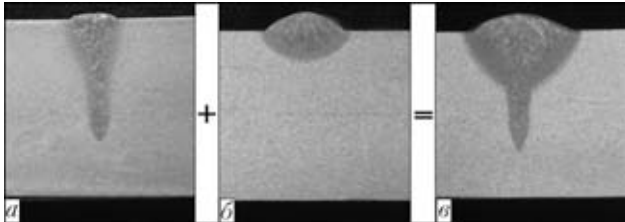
Макрошлифы швов, выполненных лазерной (а), дуговой (б) и лазерно-дуговой (в) сваркой
